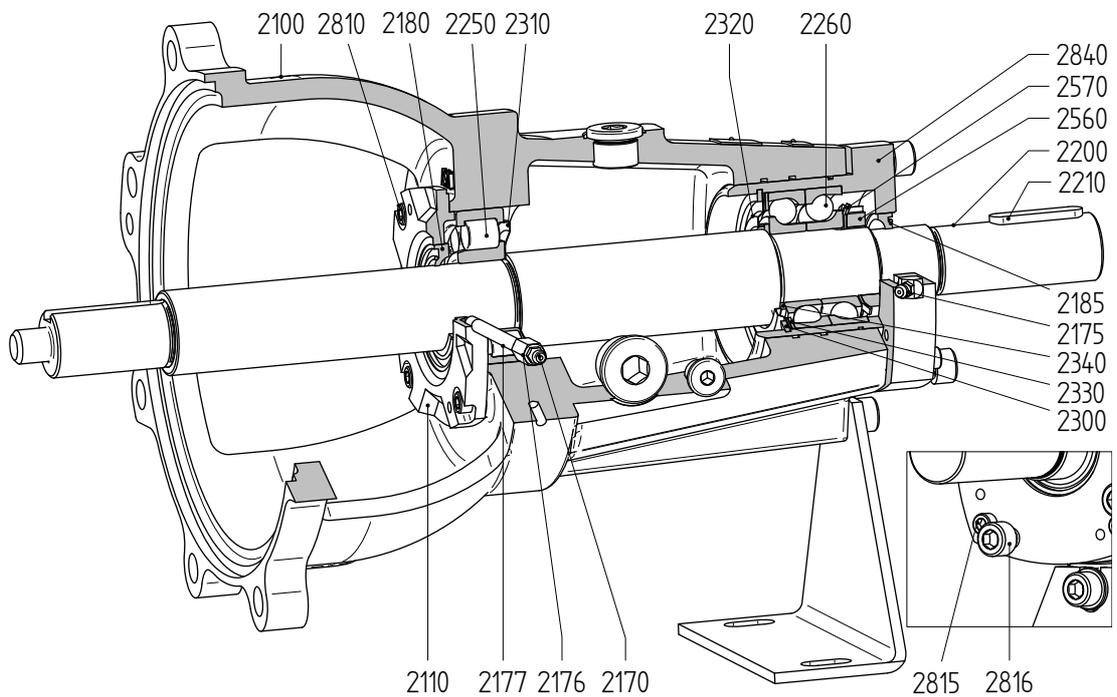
Подшипник L5 (усиленный, с консистентной смазкой, регулируемый)
